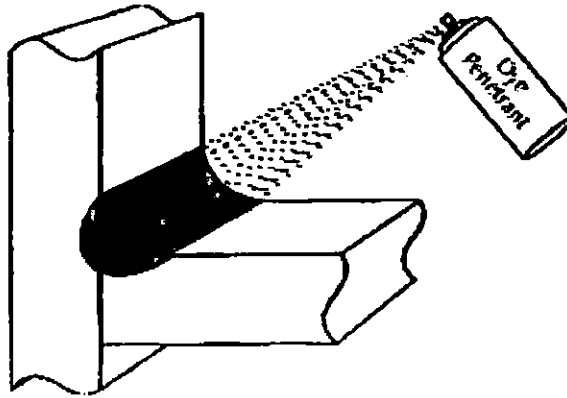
Aplicación de un líquido penetrante en forma de spray sobre una junta de soldadura, para detectar defectos no apreciables a simple vista ni a pruebas de VT. ⁽¹⁻³⁴⁾
